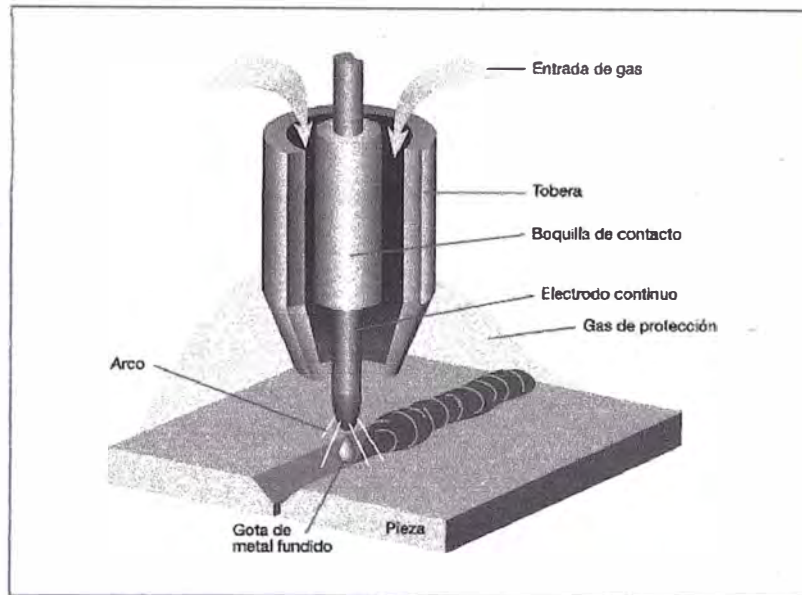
Esquema Proceso GMAW (Fuente: Manual de Soldadura Indura)
